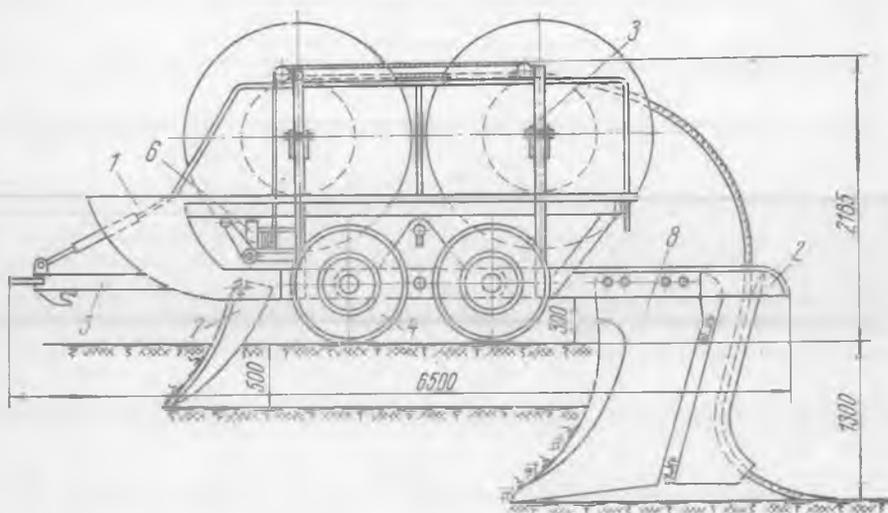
Конструкция кабелеукладчика КУ-120:
